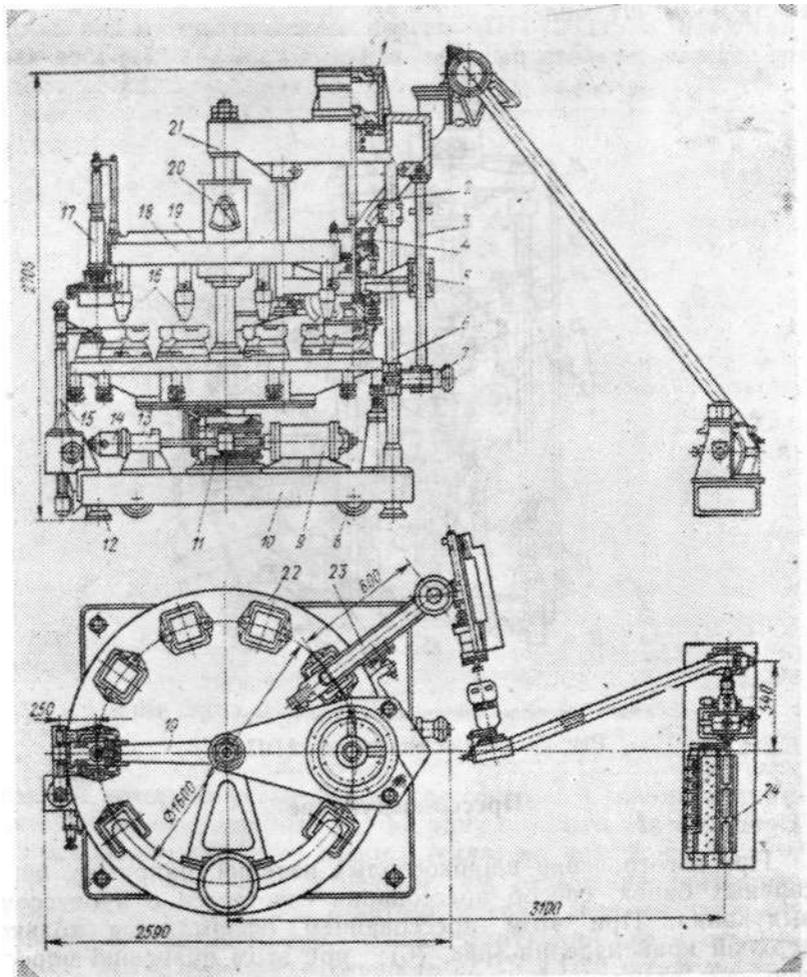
Автоматический пресс АПБ-10 для прессования стеклоолоков.
